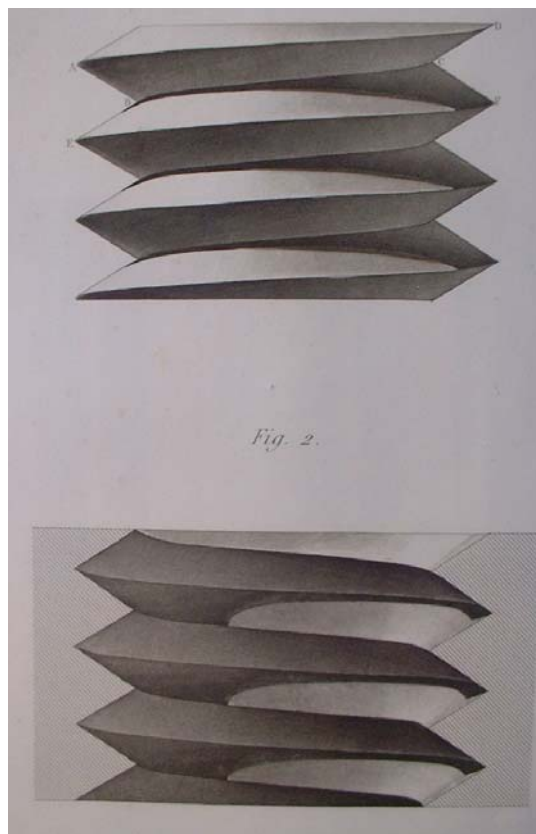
, Pl 60, machine soufflante, Leblanc, 40x22 cm
